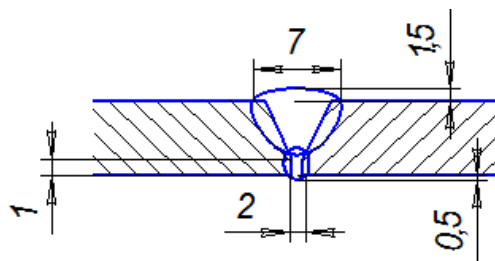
Поперечное сечение сварного соединения.
